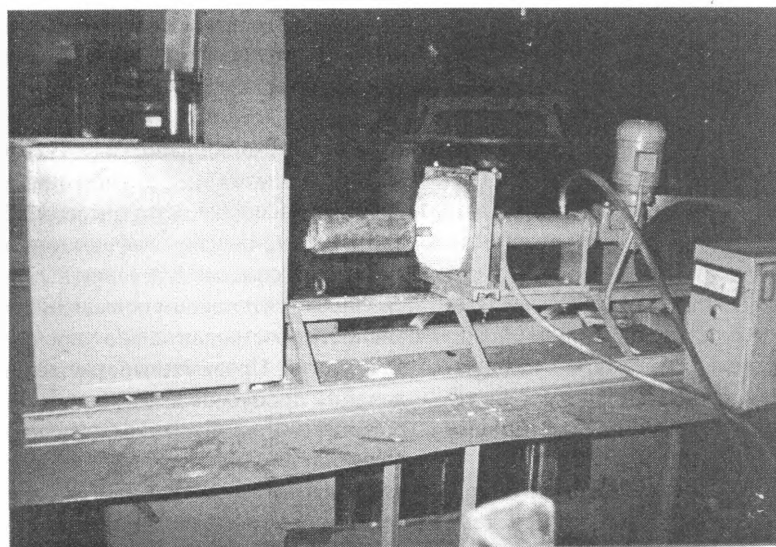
Внешний вид установки диффузионного легирования наплавочных металлических порошков, изготовленной для ОАО «Минский подшипниковый завод»
